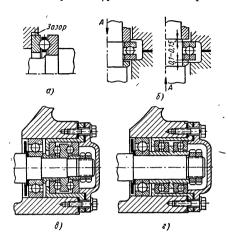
Схемы установок упорных подшипинов: a — одинарный подшипиник для односторонней осевой нагрузки; b — то же для реверсивной нагрузки (d — осевая нагрузка); b — двойной подшипник в стакане; b — два одинарных подшипника в стакане для реверсивной нагрузки
